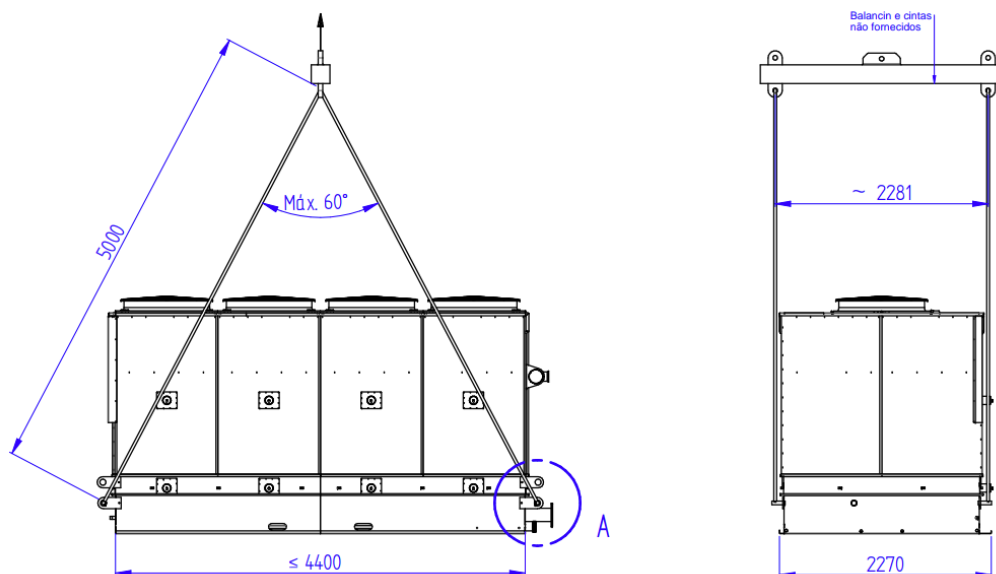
Instruções de movimentação para equipamentos com menos de 4400 mm de comprimento.
